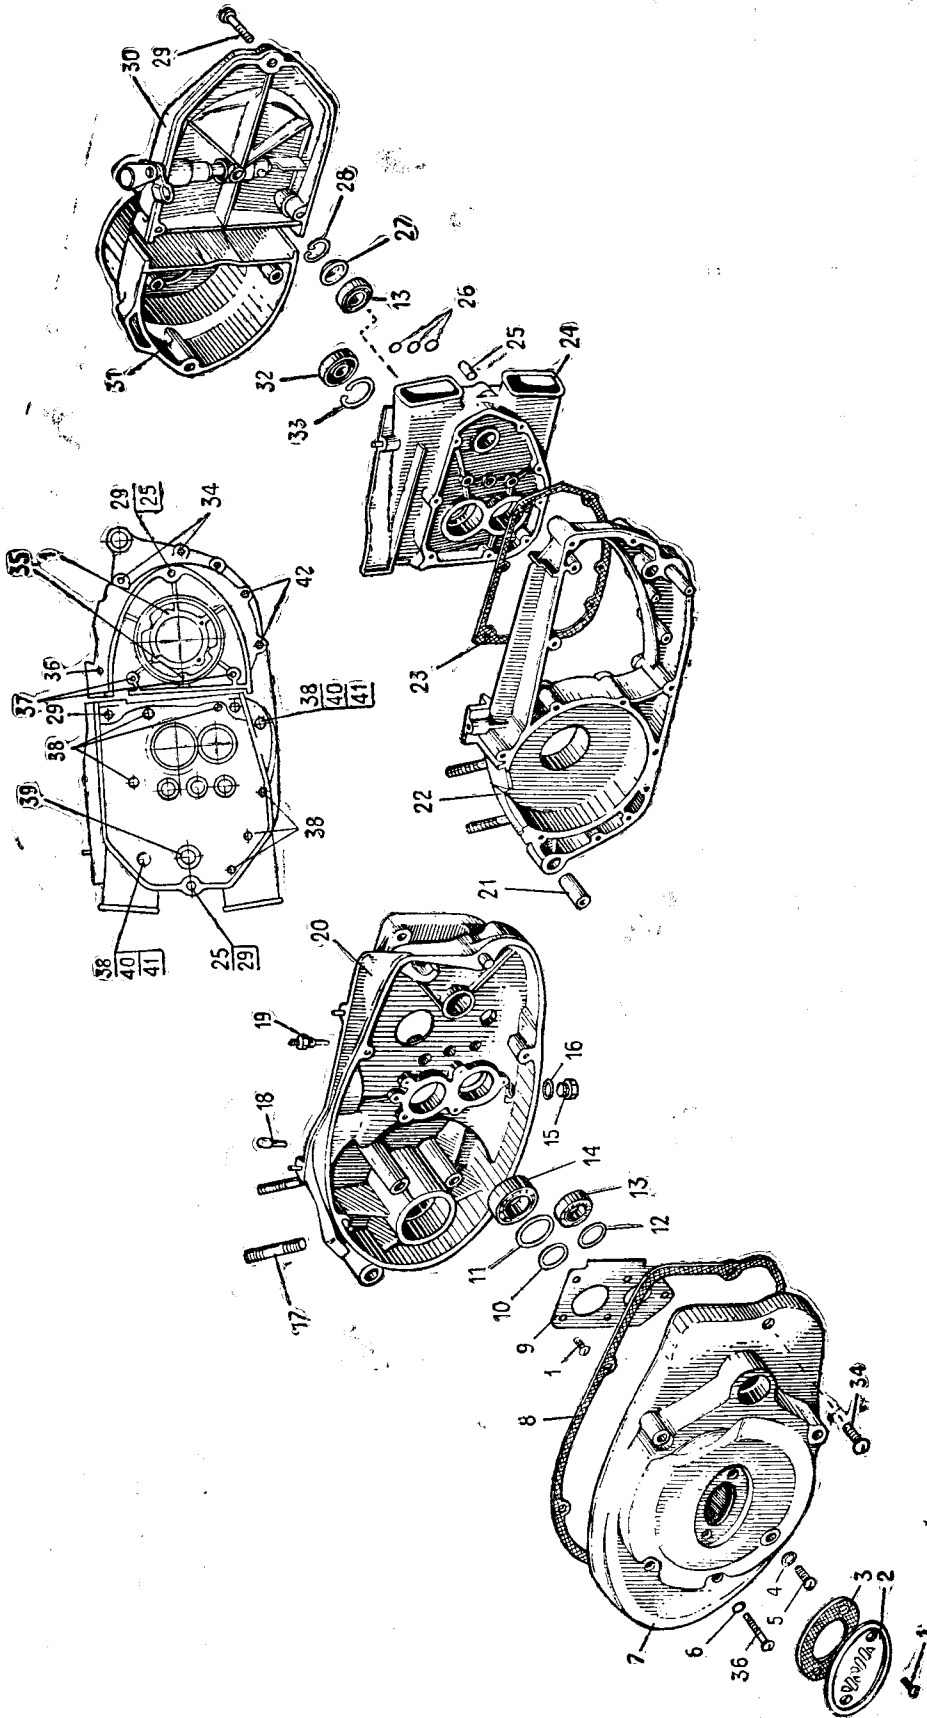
Картер с деталями для совместной системы смазки А1.03
